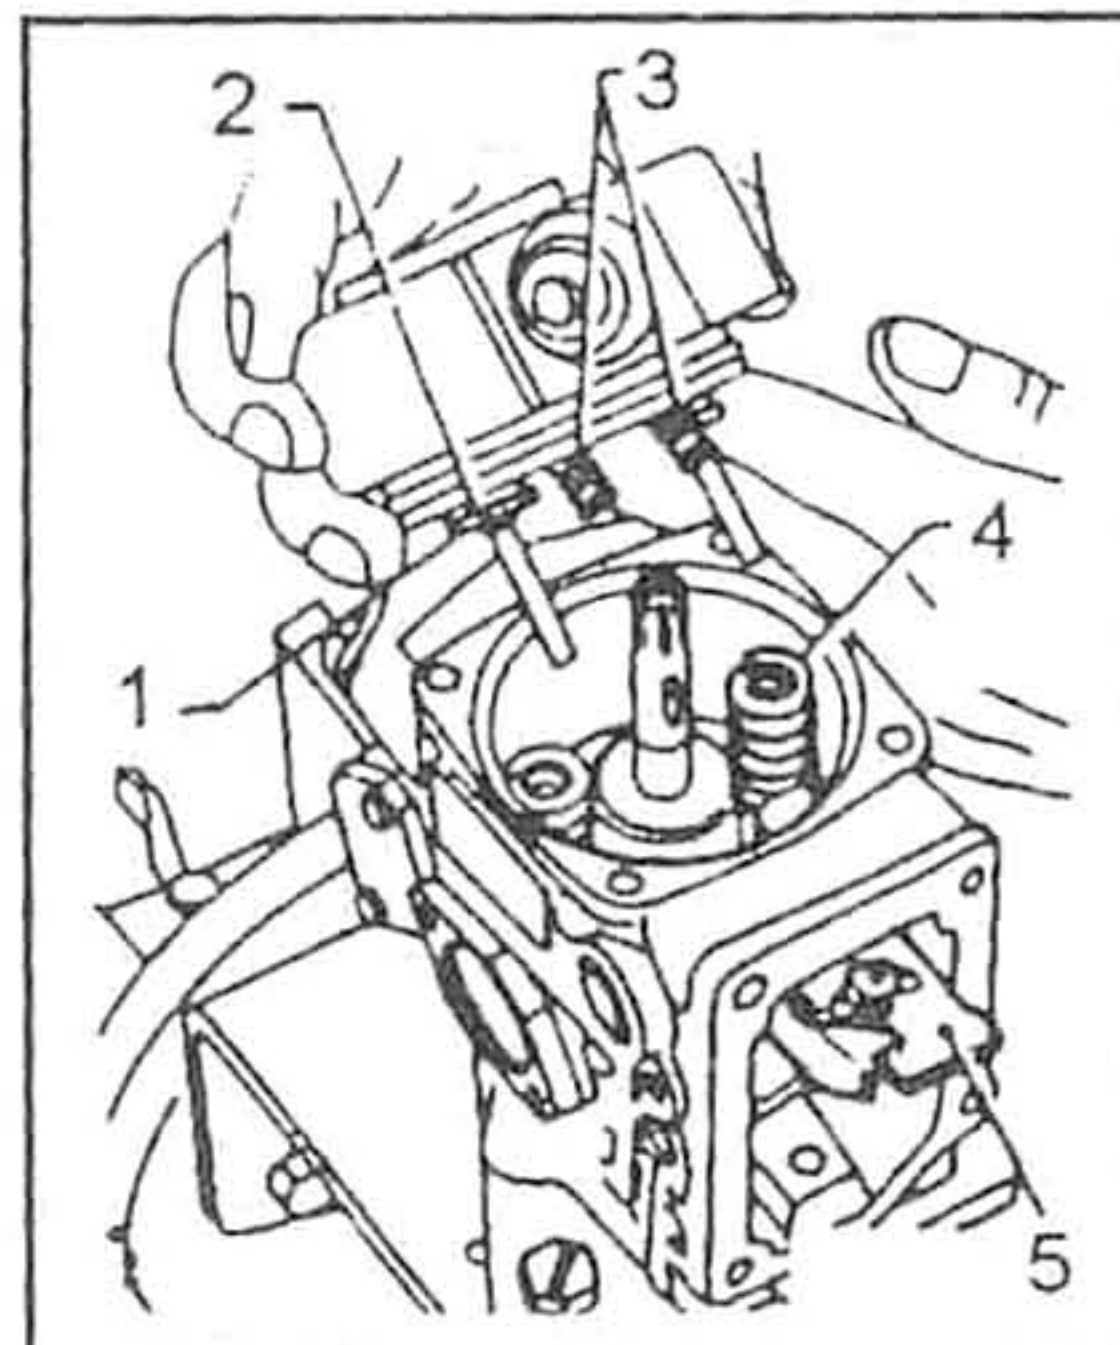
1. Опорный элемент пружины. 2. Прокладка. 3. Опорные пружины. 4. Пружина плунжера. 5. Рычаг регулятора.
